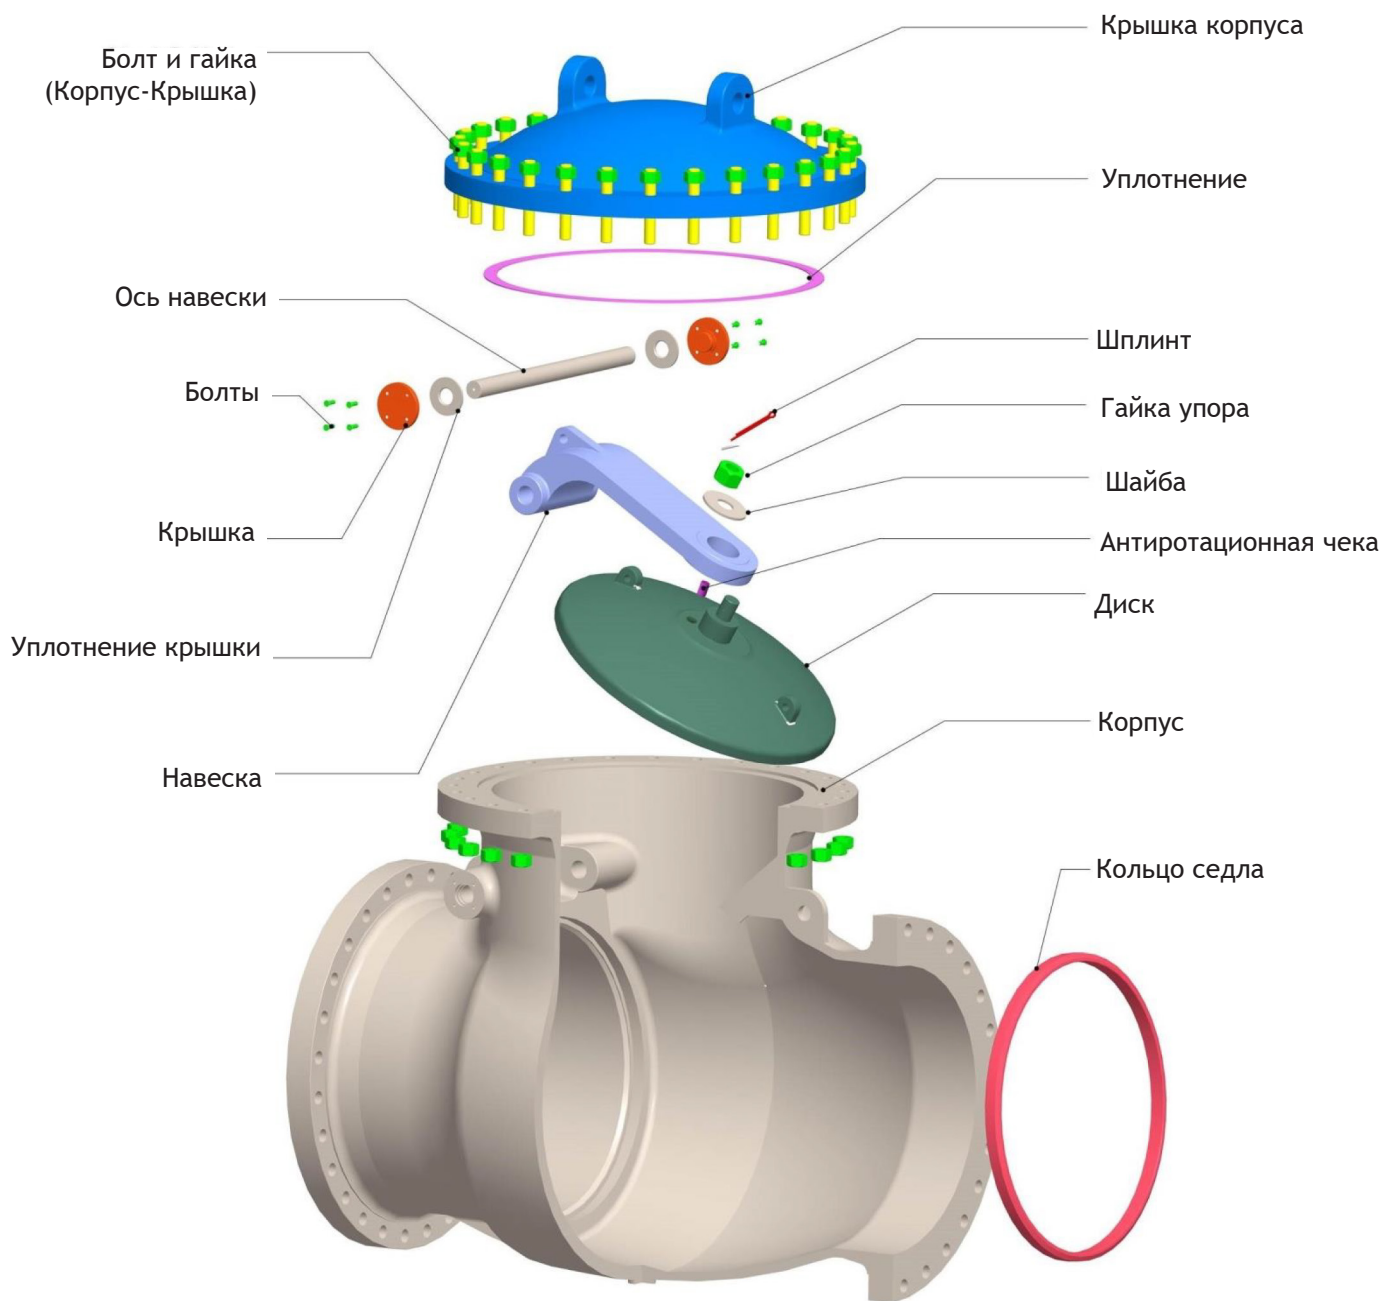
Поворотный обратный клапан (Крышка соответствует MESG) - типовой
